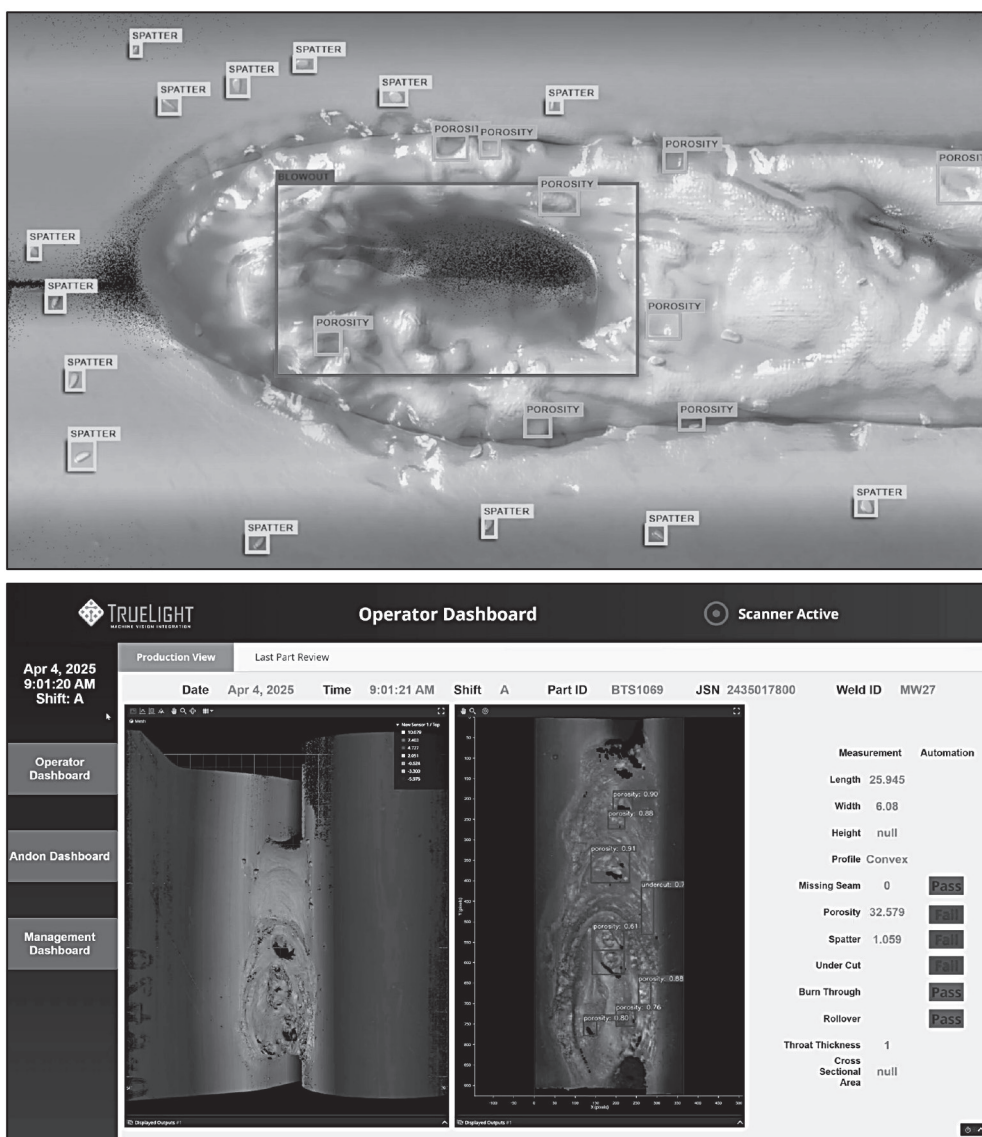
TrueLight 3DAI Weld Inspection Platform software pentru control vizual utilizând AI [28]
